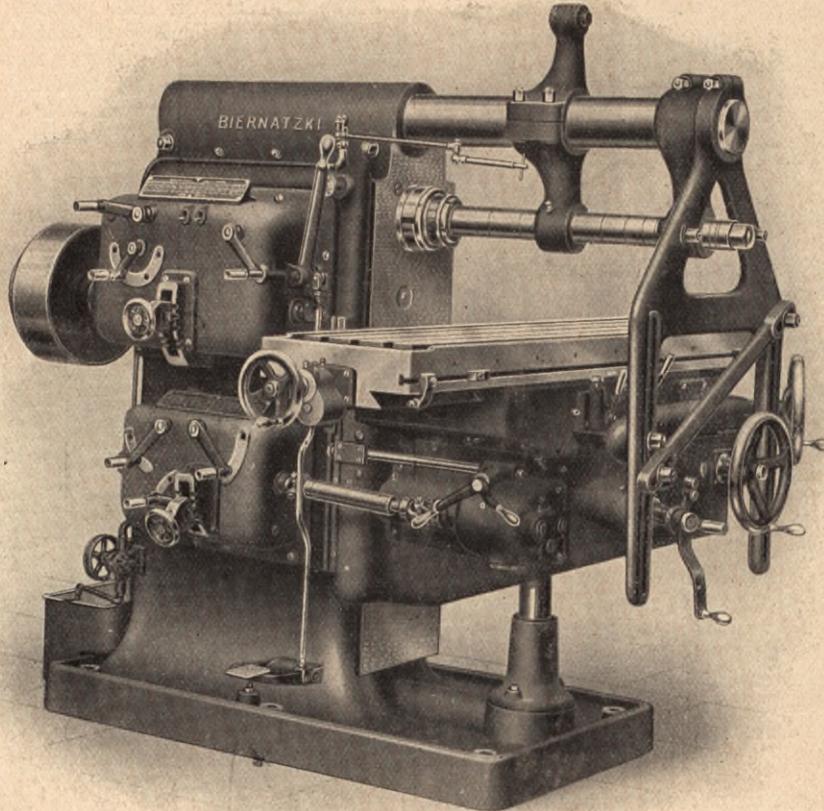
Horizontal-Hochkraft-Fräsmaschine.
